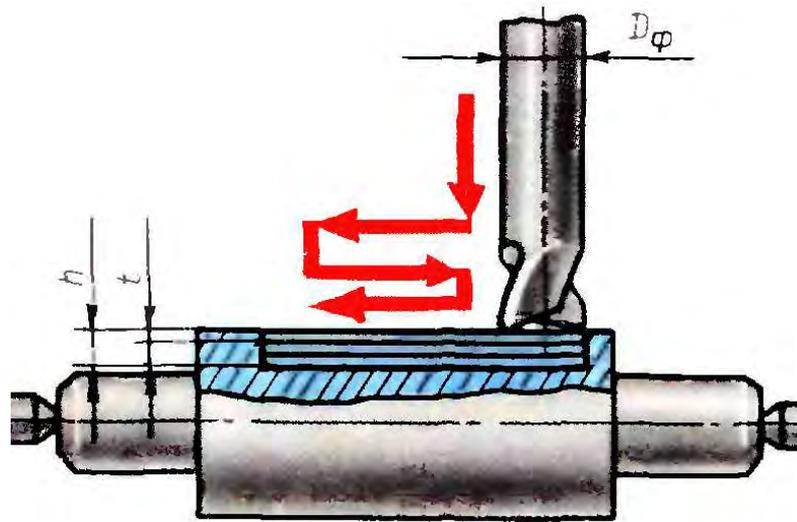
Схема фрезерования шпоночных пазов способом «маятниковая подача»
